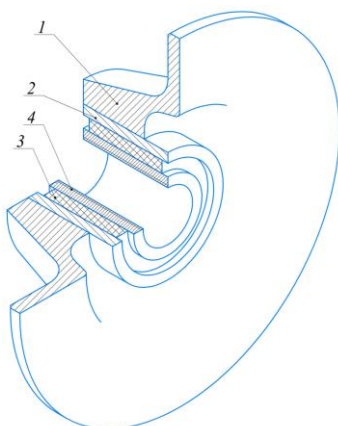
Предлагаемая бобышка кожуха зубчатой передачи
